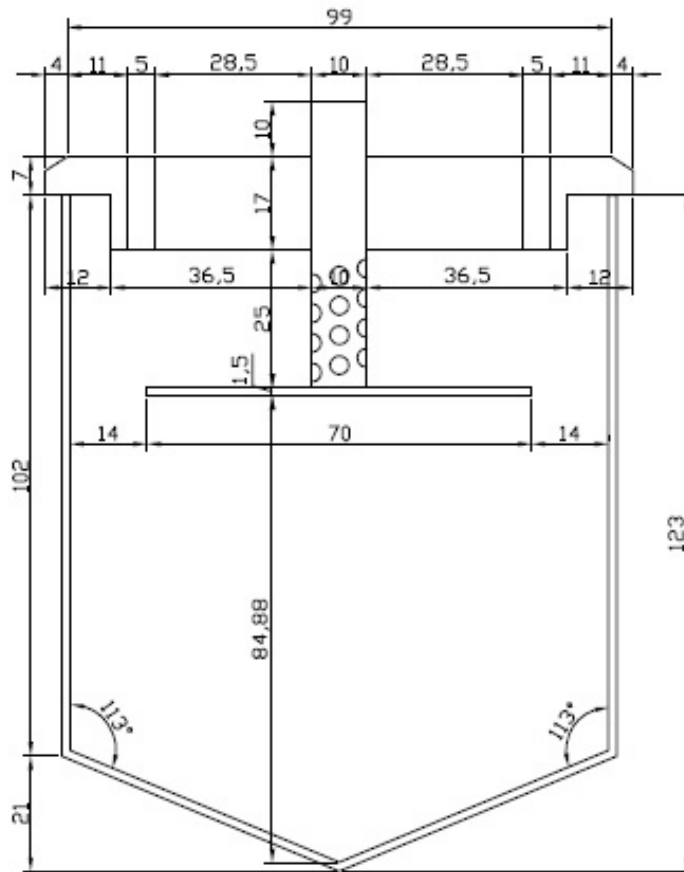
Vista geral e detalhes construtivos do primeiro modelo de DEC construído
